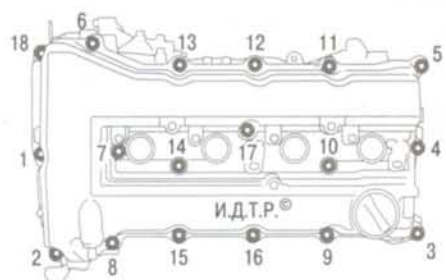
Порядок выворачивания болтов крепления крышки головки блока цилиндров
